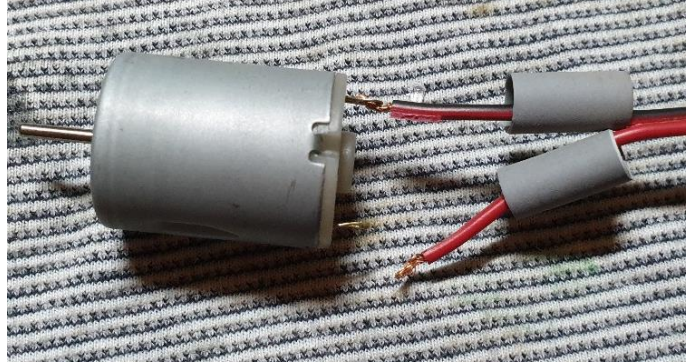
Cables soldats al motor DC 12 V (Font pròpia)
